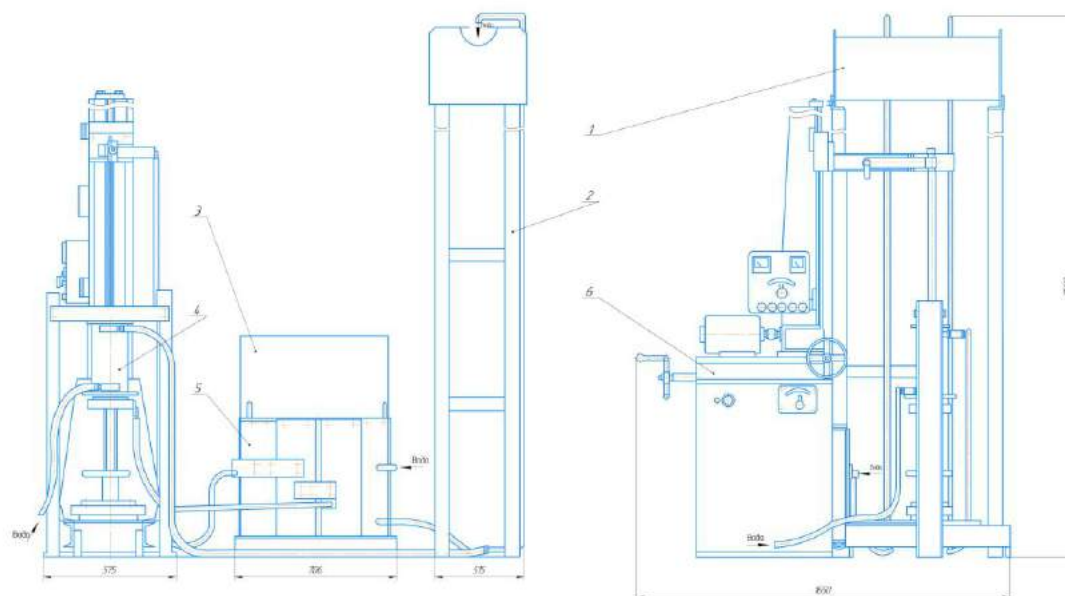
Установка для электрошлакового зварювання А-550
